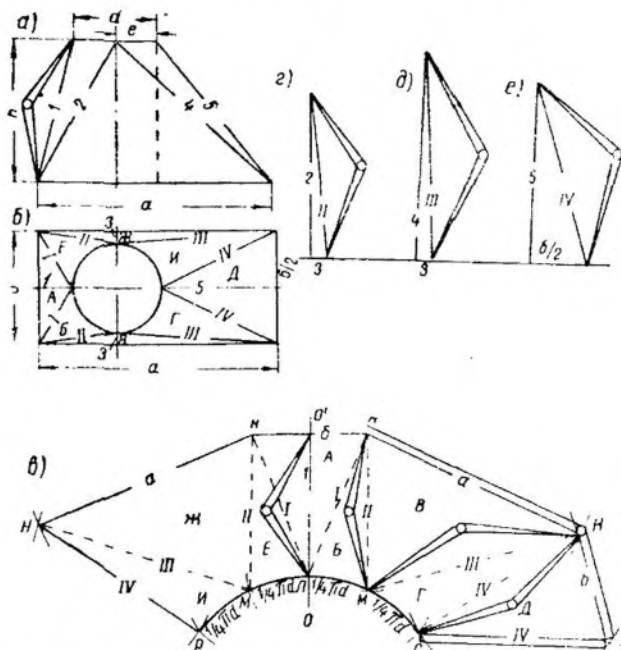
Развертка косо́го перехода с прямоугольного на круглое сечение
